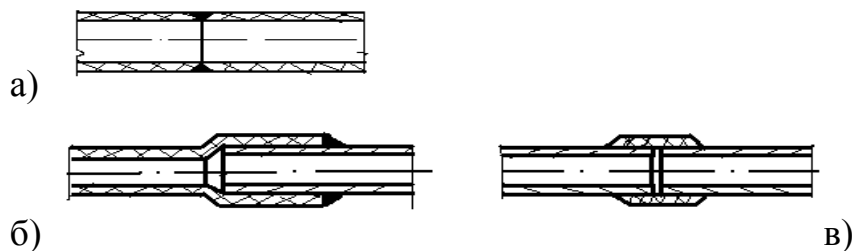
Сварные неразъемные соединения виниловых труб
